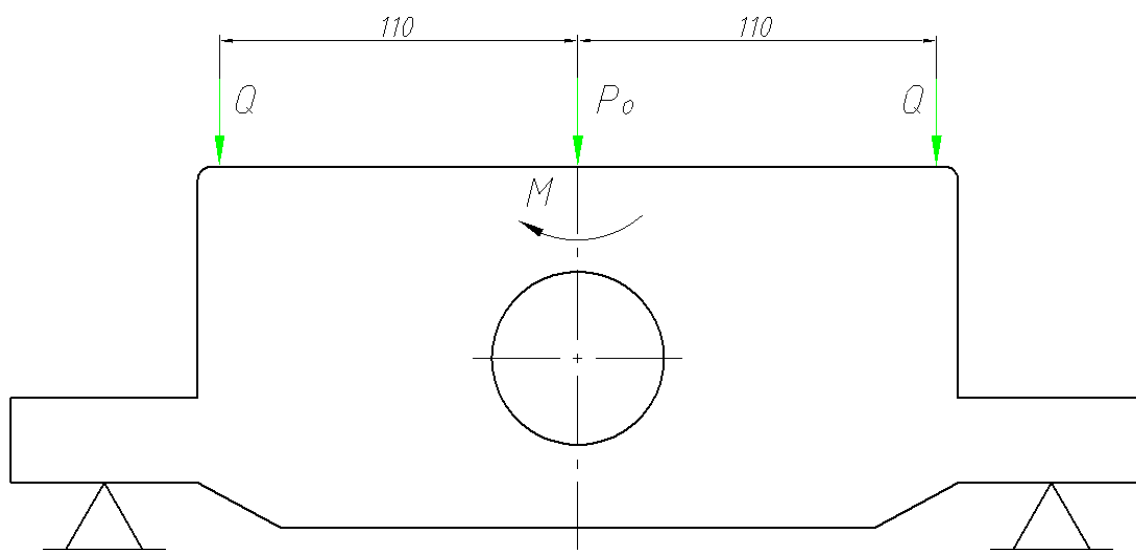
Розрахункова схема сил затиску заготовки
